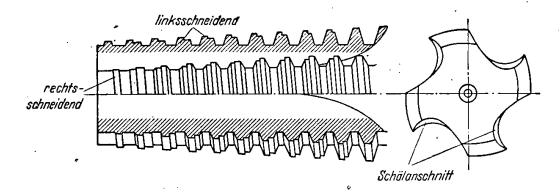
Hochleistungs-Gewindebohrer für Trapezgewinde (Hartex-Bohrer, R. Stock, Berlin)
